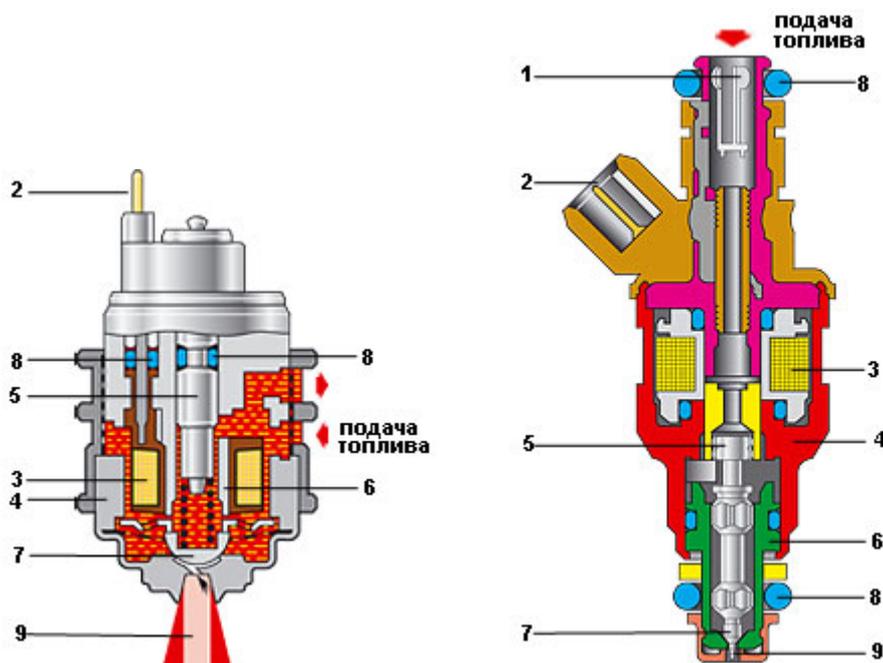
Устройство форсунки: а – форсунка центрального впрыска; б – форсунка распределенного впрыска; 1 – фильтр; 2 – контакт электрического разъема; 3 – обмотка электромагнита; 4 – корпус форсунки; 5 – сердечник; 6 – корпус клапана (а), корпус клапана (б); 7 – клапан (а), игла клапана (б); 8 – уплотнительное кольцо; 9 – распылительное отверстие
